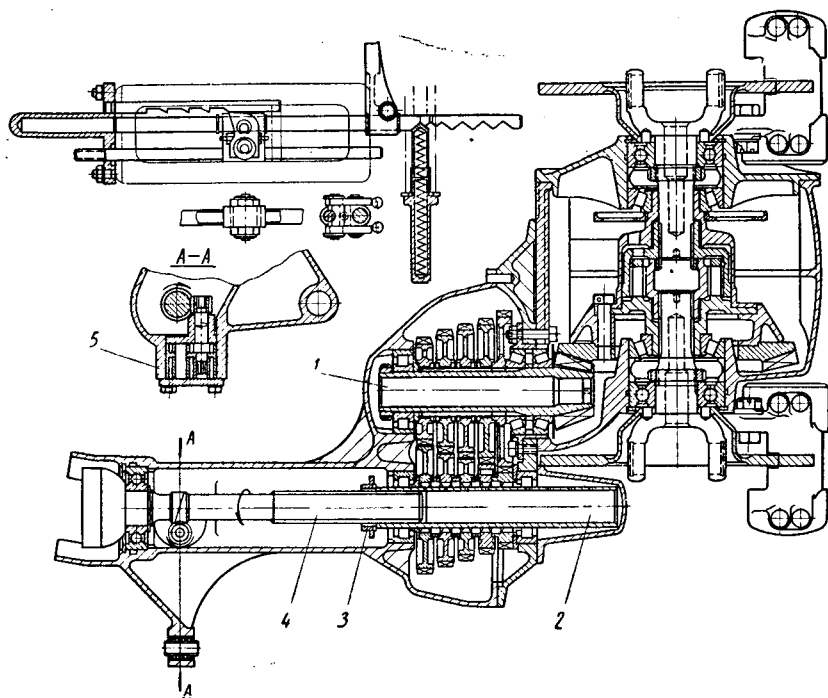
Пятиступенчатая коробка передач Лотос для гоночного автомобиля с передним расположением двигателя.
